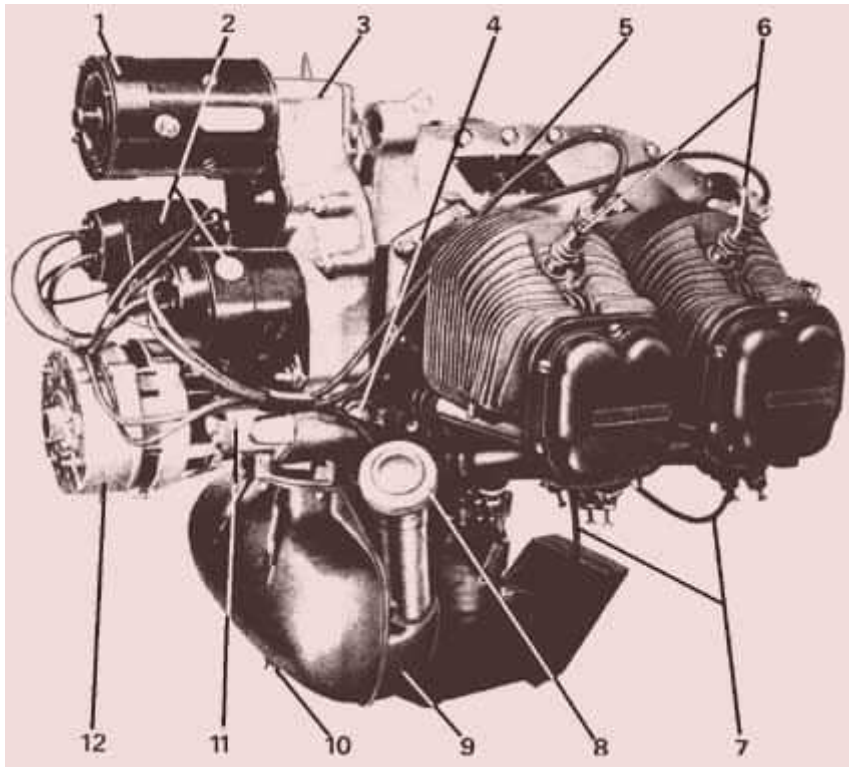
Moteur d'avion léger à 4 cylindres (vue arrière)
